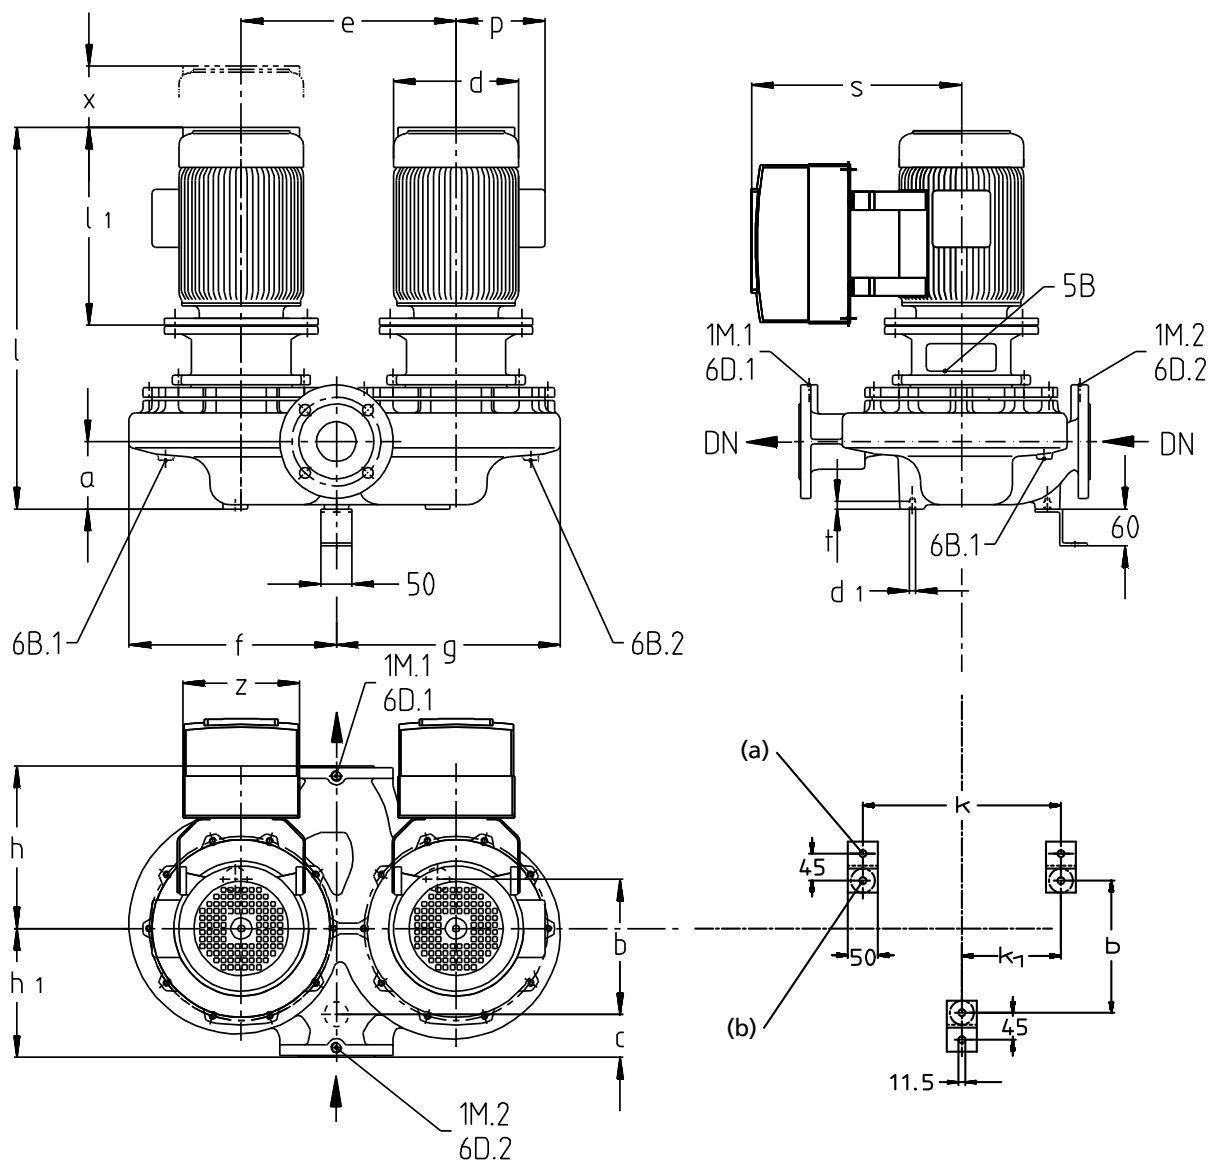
Dimensioni gruppo pompa con PumpDrive 2
